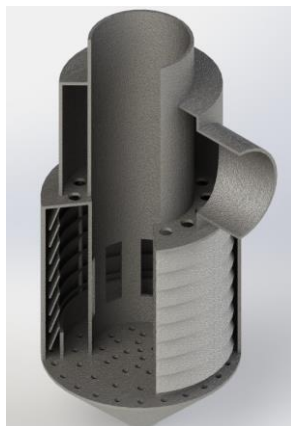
Пылеуловитель с соосно расположенными трубами (вид с разрезом)
